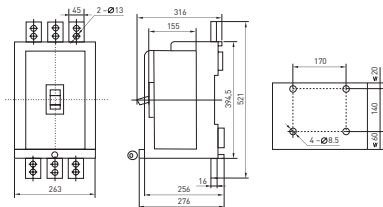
Габаритные и установочные размеры автоматических выключателей
